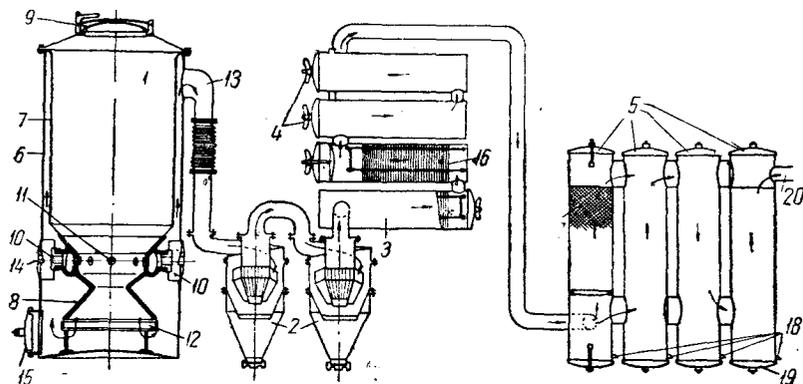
Схема газогенераторной установки Г-25 для трактора СГ-65:
